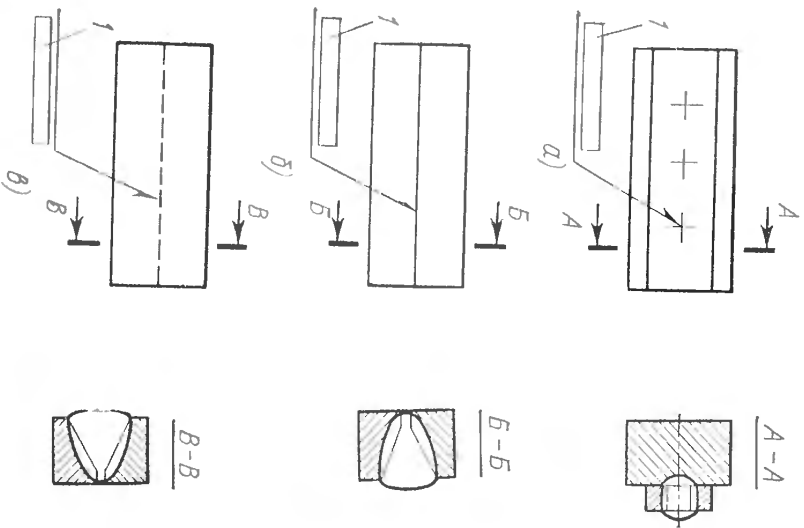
Условные изображения видимых и невидимых швов сварных соединений:
